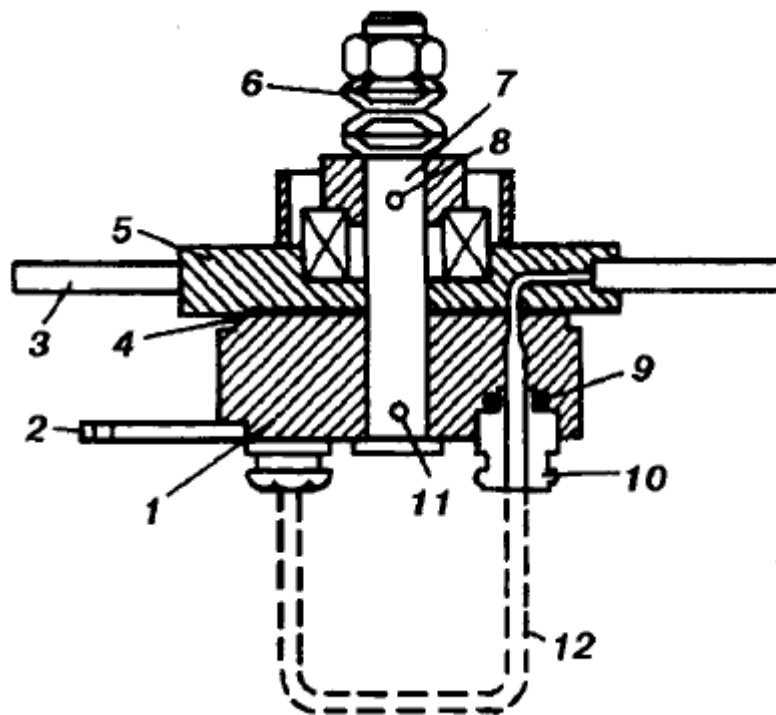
Газовий кран – дозатор: 1 – поворотна головка; 2 – вушко; 3 – фланець; 4 – ущільнювальна прокладка; 5 – корпус; 6 – пружина; 7 – вал; 8, 11 – штифти; 9 – кільце ущільнювача; 10 – гайка; 12 – доза
